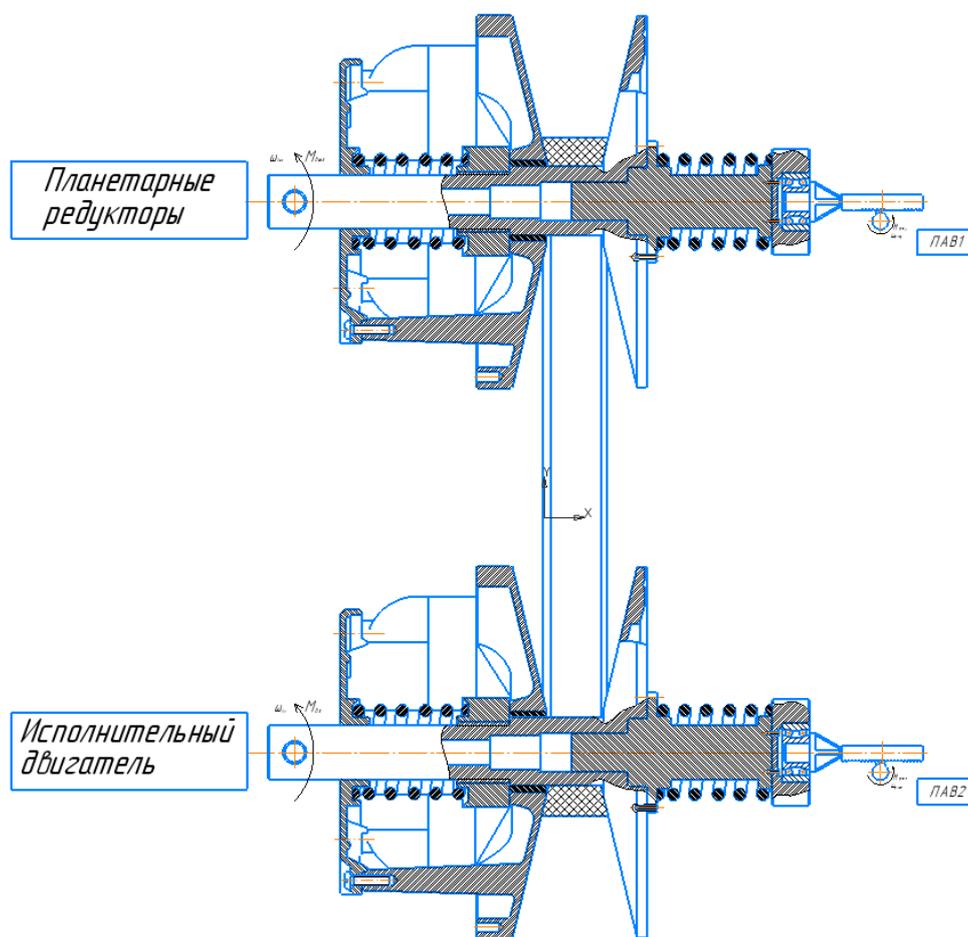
Активный вариатор на базе двух вариаторов «Сафари»
